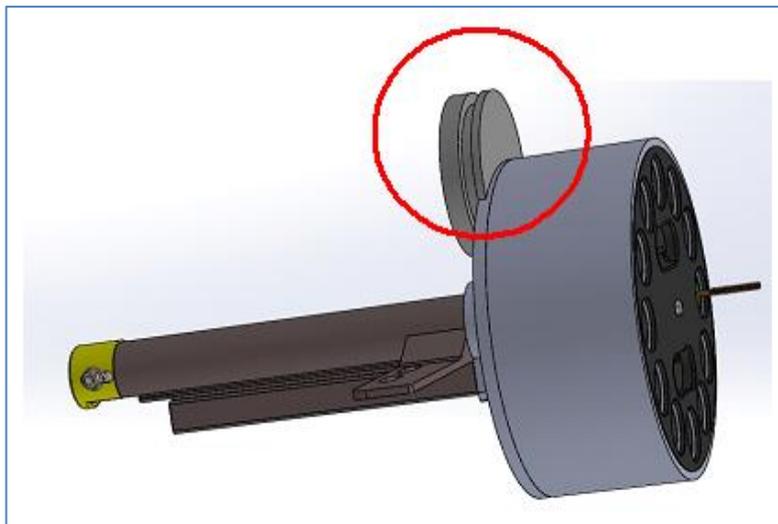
Instalador de Calibradores con Acoplamiento Mecánico.
